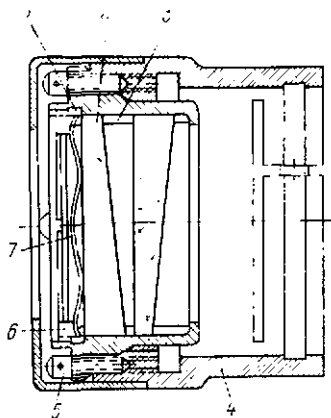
Разрез дальномерной насадки ДН-04 (ДД-3)
